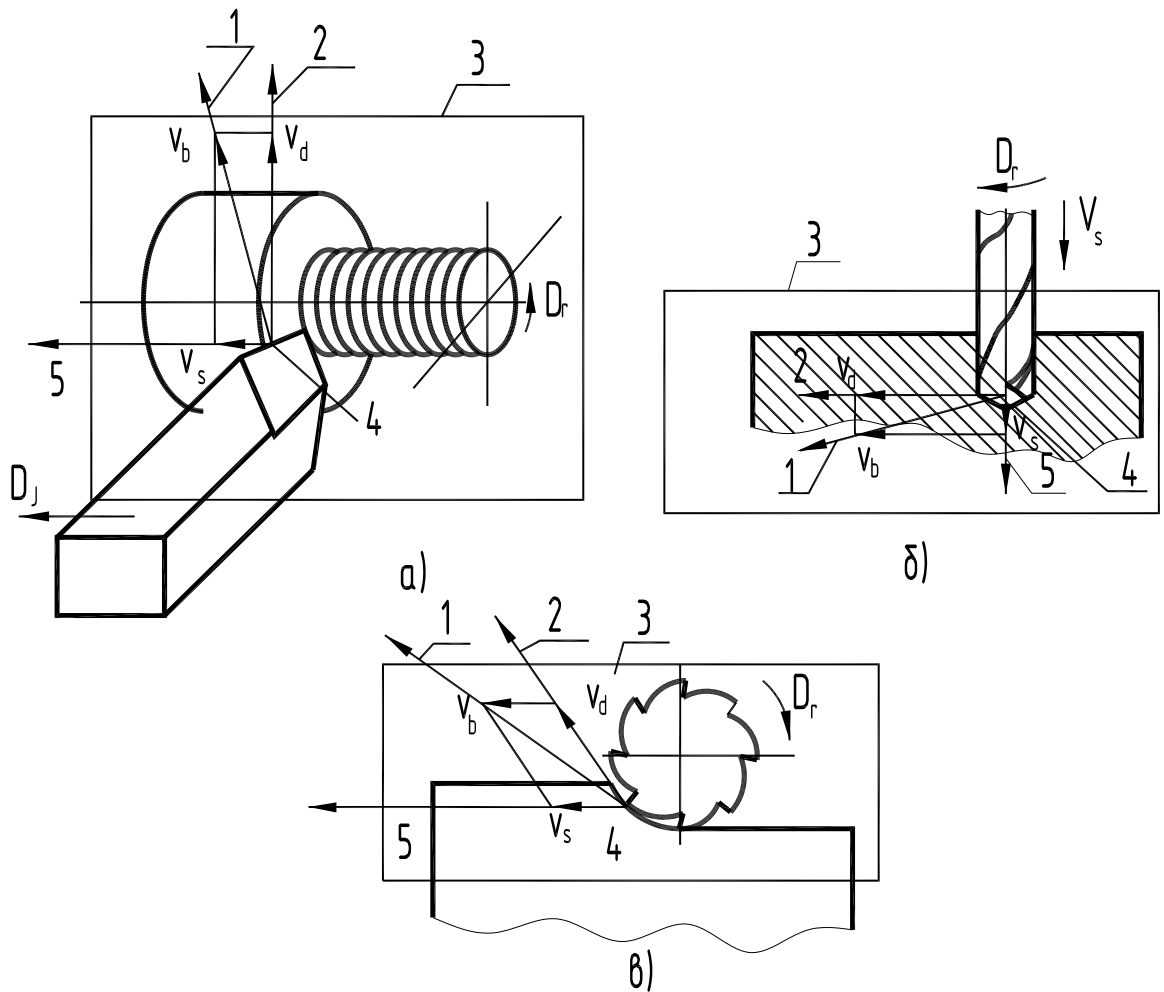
Схема элементов движений в процессе резания при обтачивании (а), сверлении (б) и фрезеровании(в)
